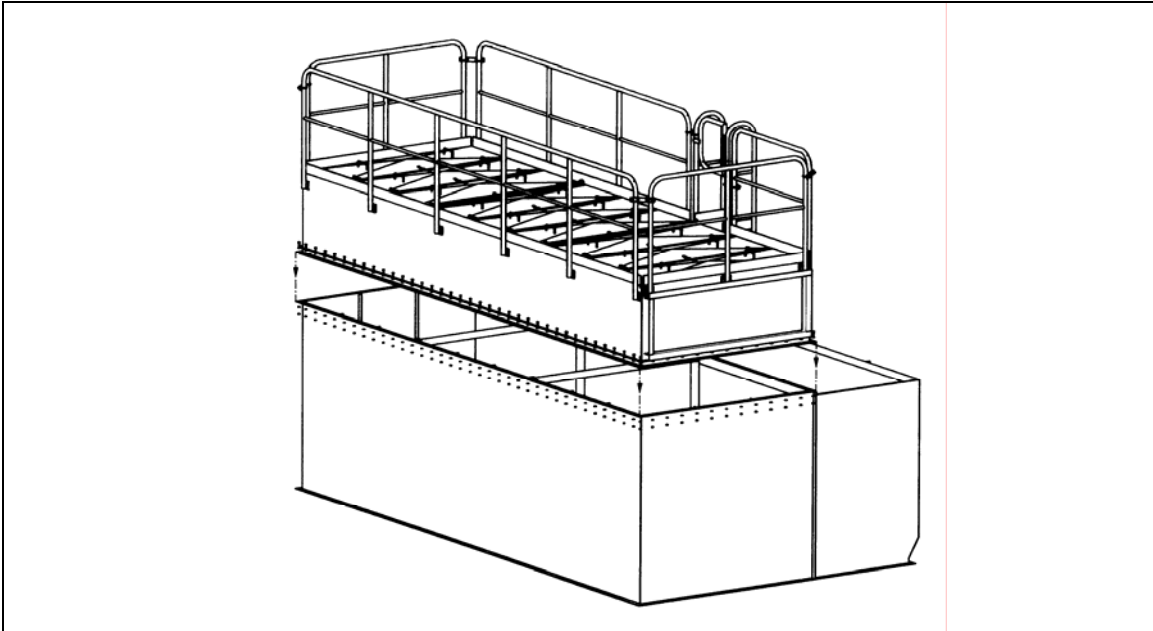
Сборка верхней камеры загрязненного воздуха
